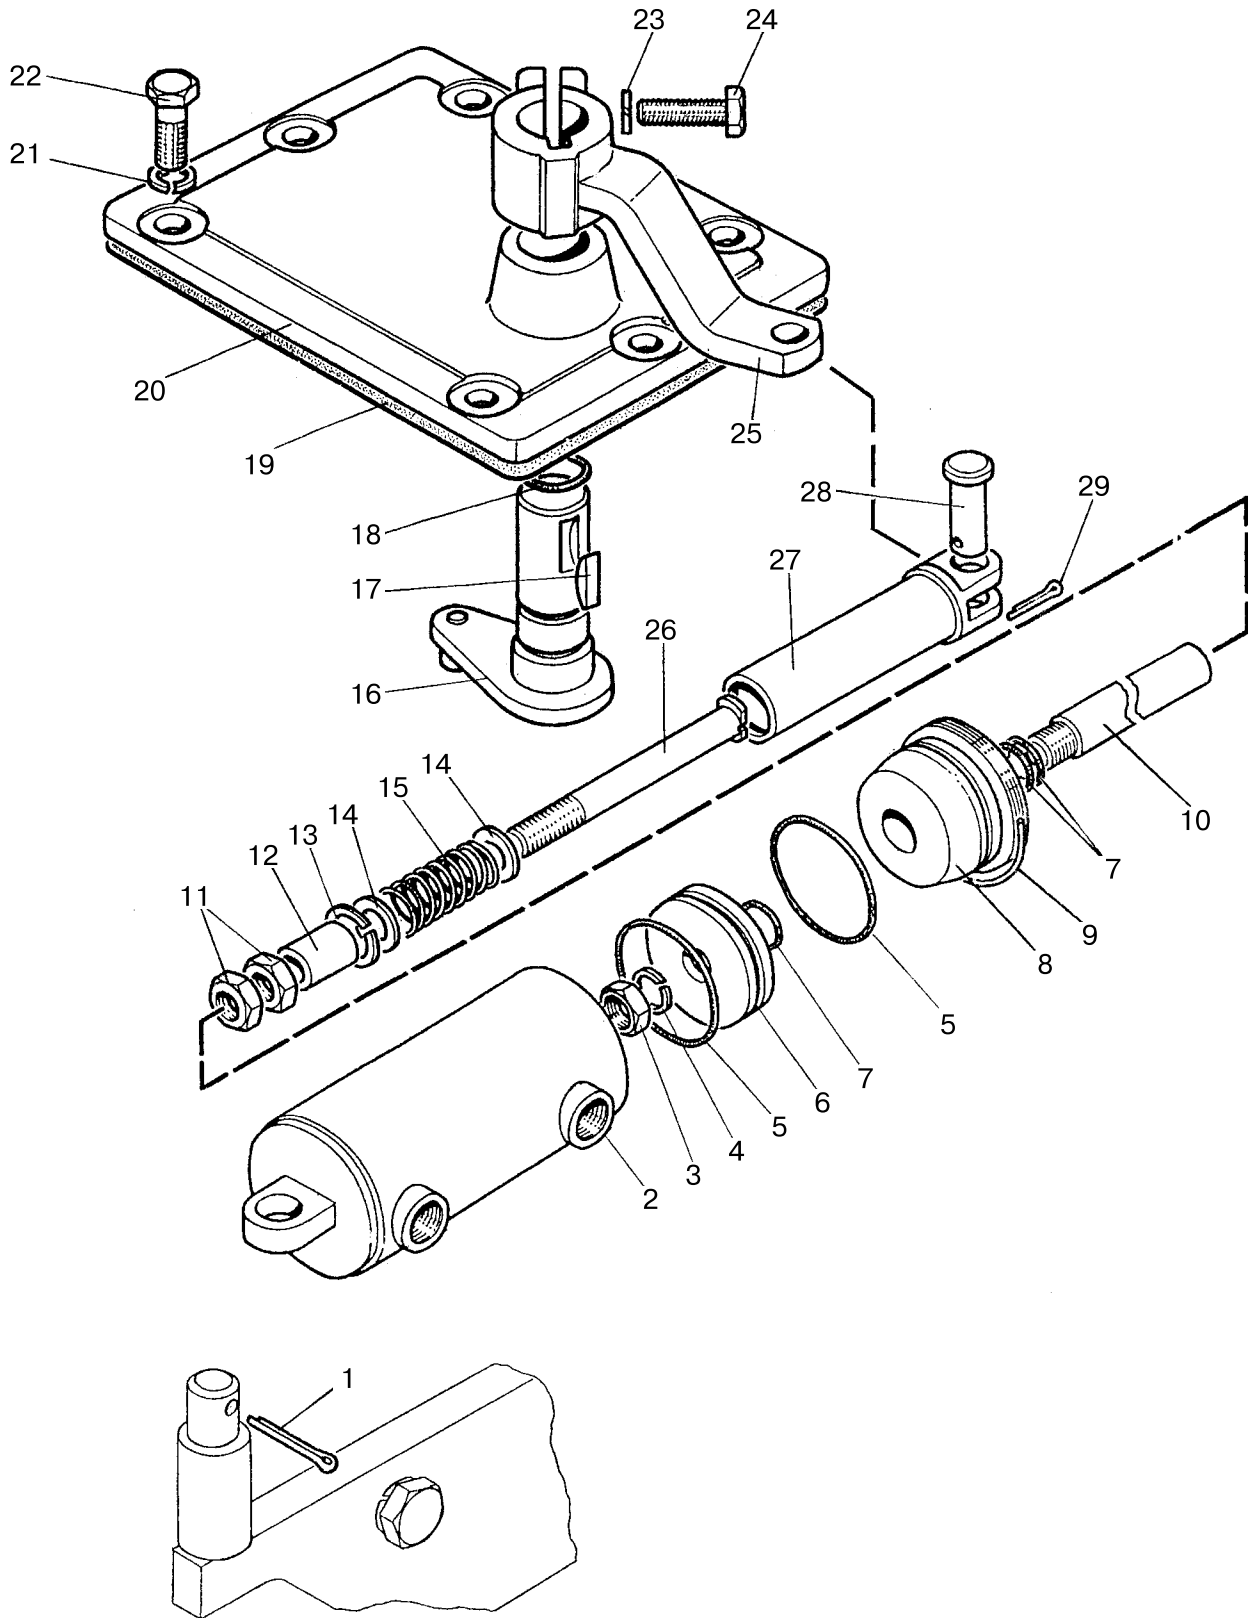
Mecanismo de cambio de marchas. Guerpo de horquillas
